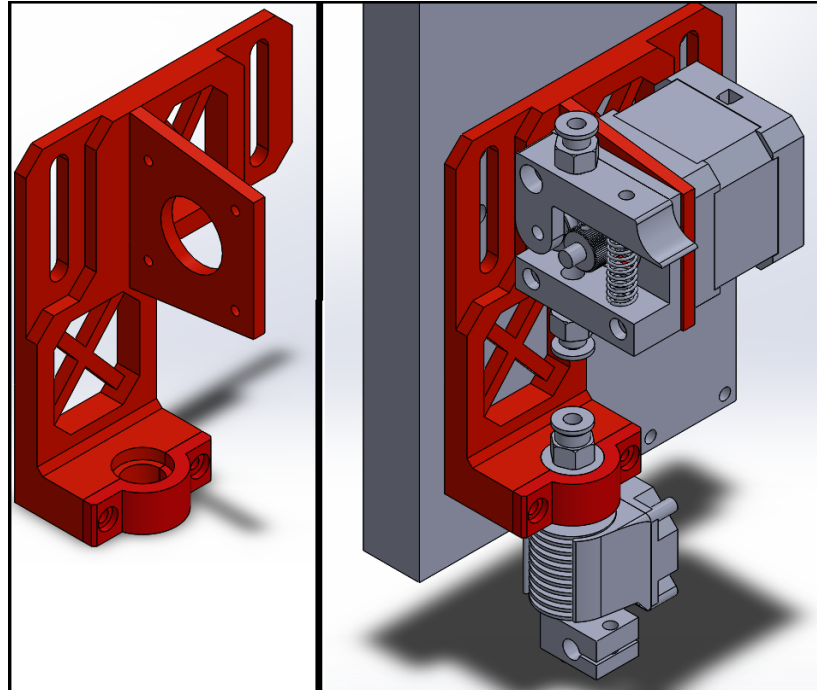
Suporte da extrusora da empresa GeeTech
